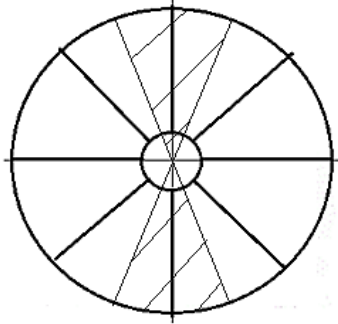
Розрахункова схема радіального розташування опорних балок під тарілки
